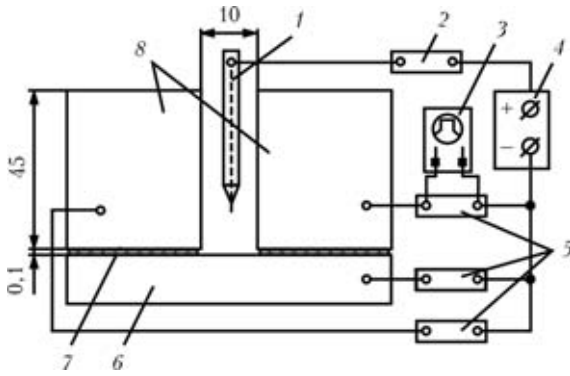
Схема установки для измерения тока, протекающего через боковые стенки разделки при СУЗ с управляющим магнитным полем: 1 — вольфрамовый электрод; 2 — шунт для измерения сварочного тока; 3 — осциллограф; 4 — источник питания; 5 — шунты для измерения тока, протекающего через боковые и нижнюю стенки; 6 — нижняя стенка разделки; 7 — изолятор; 8 — боковые стенки
